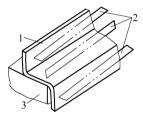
检查工件平面度 1—工件 2—钢直尺 3—平台
